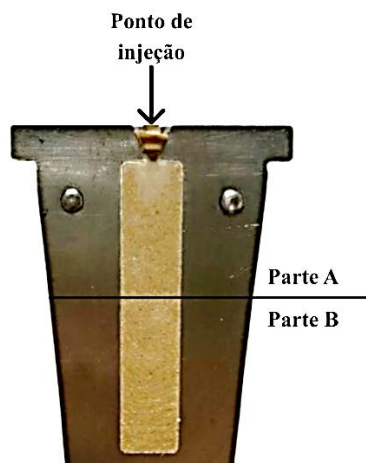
Partes do corpo de prova no molde da injetora tipo pistão.
